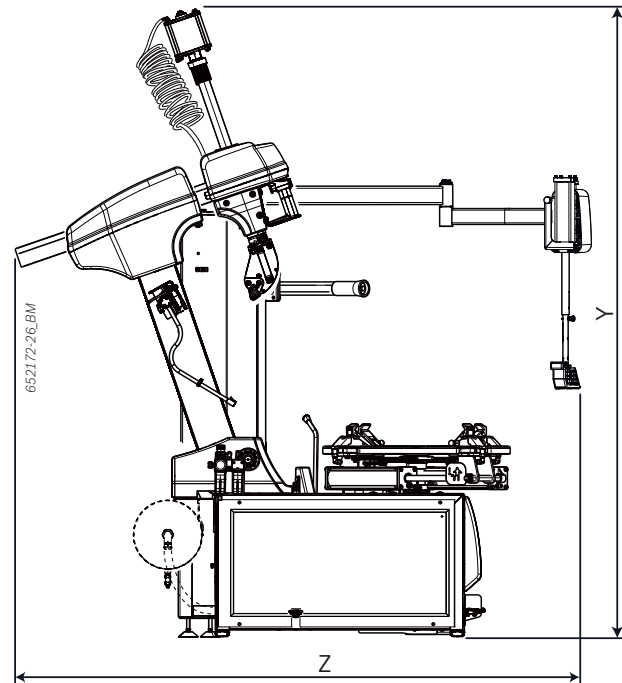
Dimensiones vista frontal FALCO EVO 628 S (IT) V8
